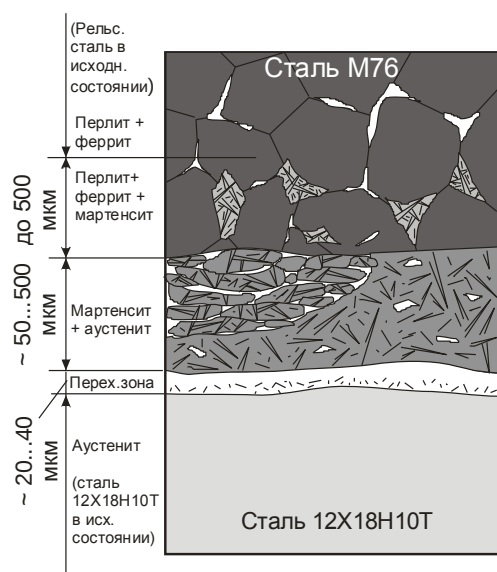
Схема строения сварного шва между рельсовой сталью и хромоникелевой вставкой
